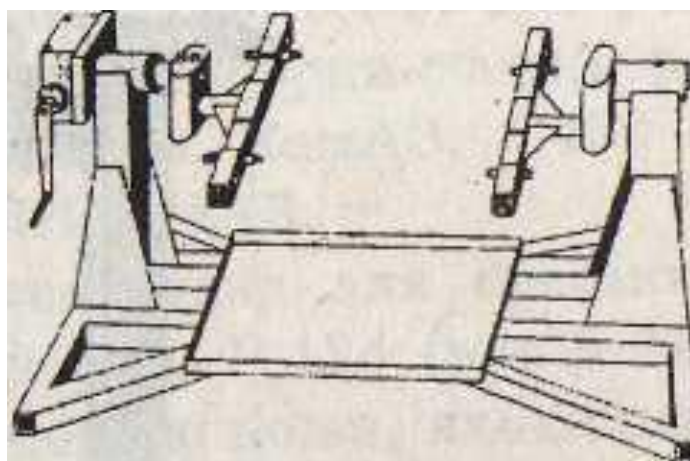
Общий вид стендов для разборки- сборки двигателей Р-770
